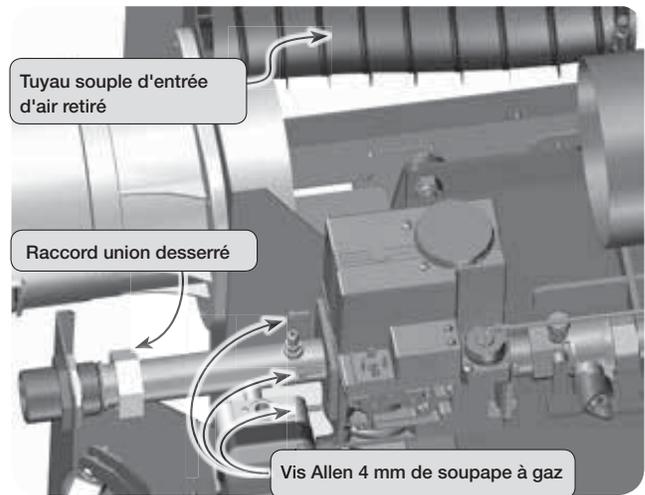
Plaque de recouvrement prête pour la dépose et le remplacement du brûleur
